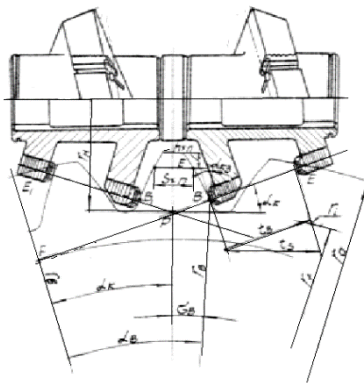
Схема верстатного зачеплення спеціальної твердосплавної фрези з колесом, що обробляється
